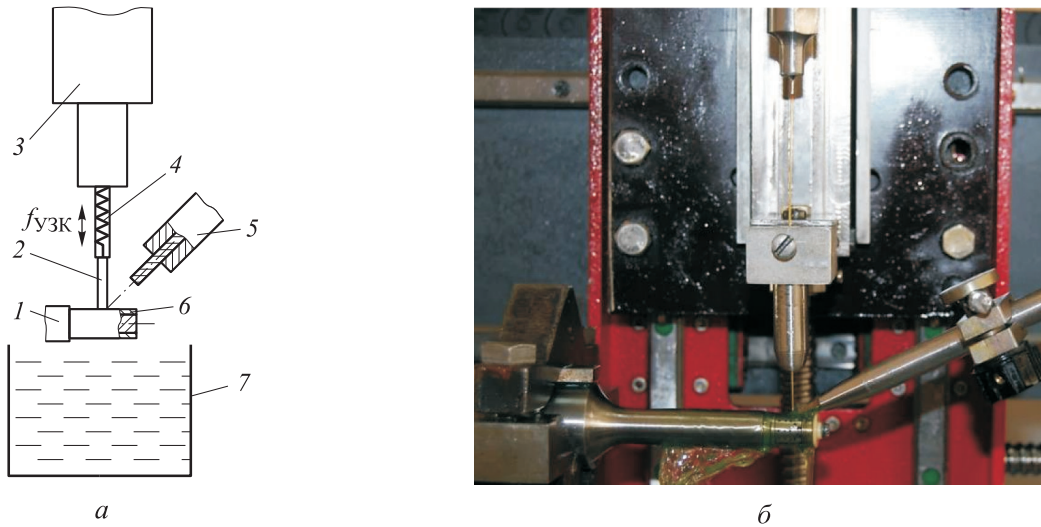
Схема (а) и внешний вид (б) установки для обработки детали с наложением УЗК на ЭИ:
